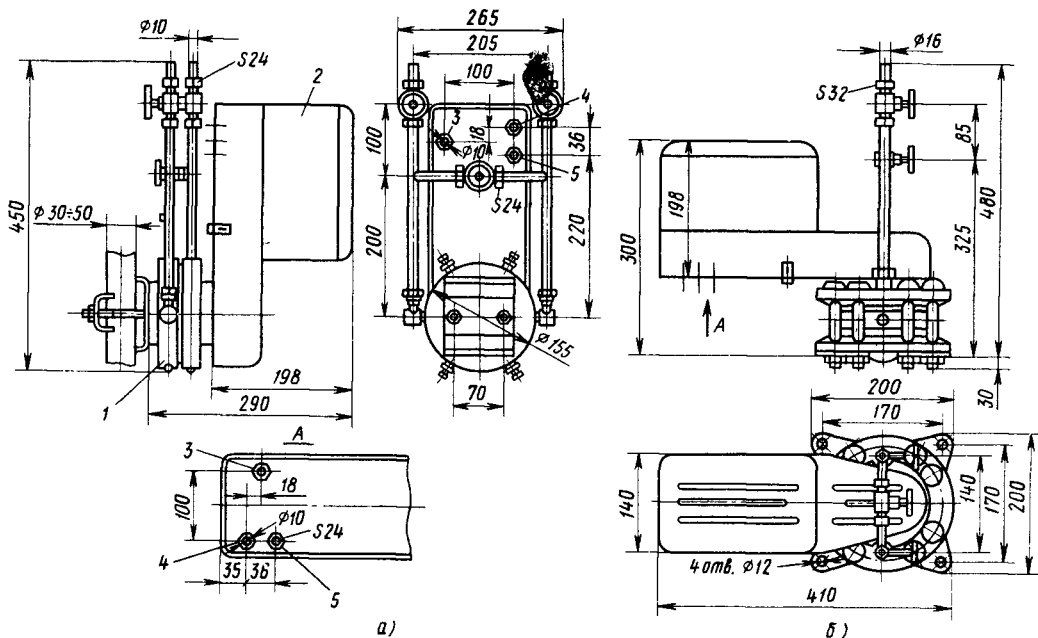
Общий вид и габаритные размеры датчиков ДРДГ-400 (а), ДРДГ-630–ДРДГ-1600 (б)
